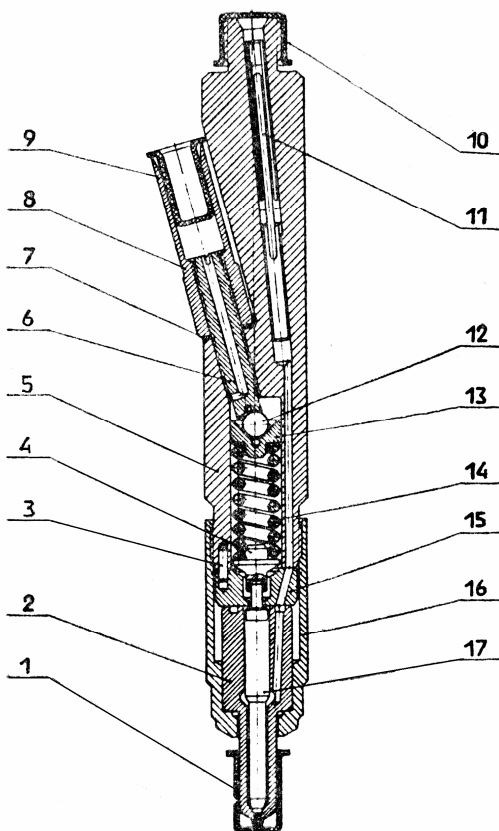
Форсунка мод. 181: 1, 9, 10 - заглушки; 2 - корпус распылителя; 3 - штифт; 4 - штанга форсунки; 5 - корпус форсунки; 6 - винт регулировочный; 7 - прокладка; 8 - гайка; 11 - стержень фильтра; 12 - шарик; 13 - верхняя тарелка пружины; 14 - пружина форсунки; 15 - проставка; 16 - гайка распылителя; 17 - игла распылителя.
